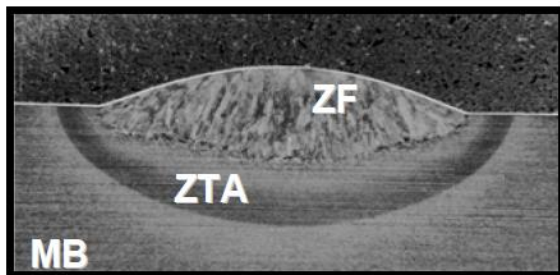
24 - Macrografia de solda obtida por simples deposição sobre chapa plana.
